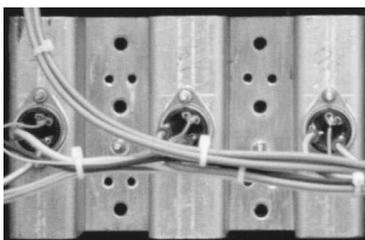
Dissipador alternativo em chapa de alumínio quinada, com 160x50x100mm
